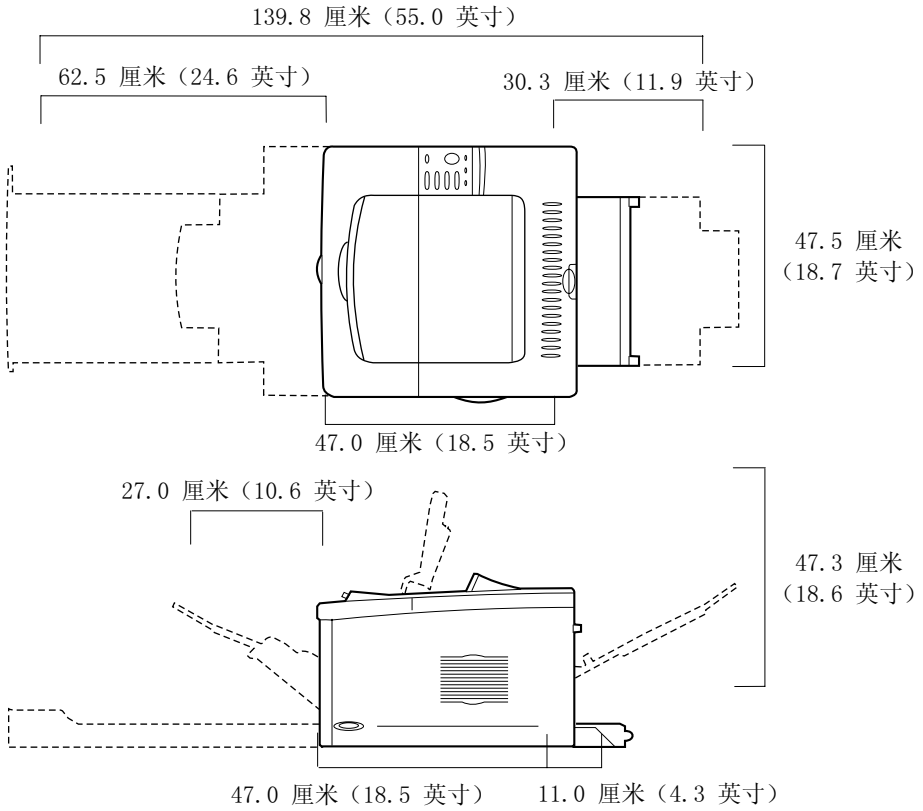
HP LaserJet 5000 打印机尺寸 (俯视图和侧视图)
